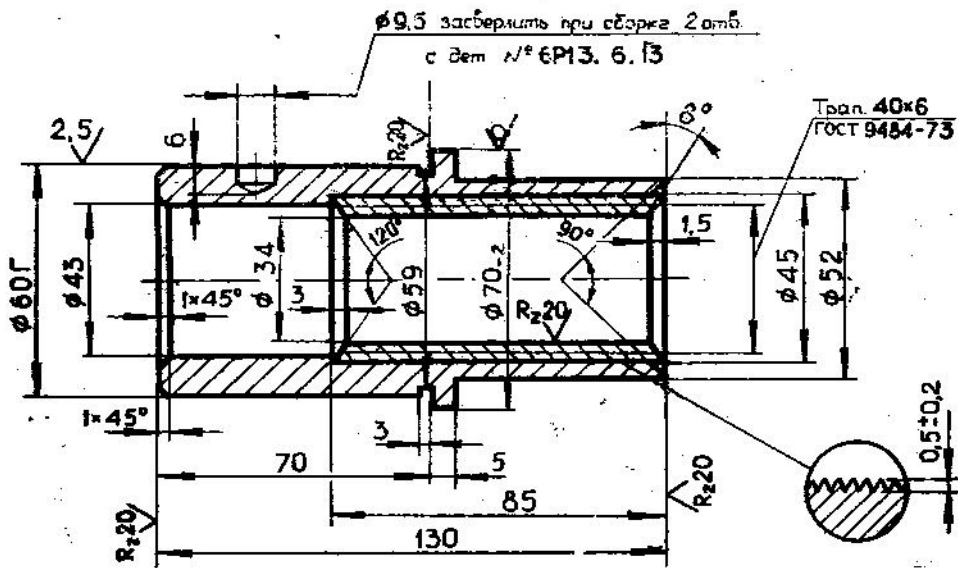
Гайка биметаллическая. Деталь 6P13.6.21A
